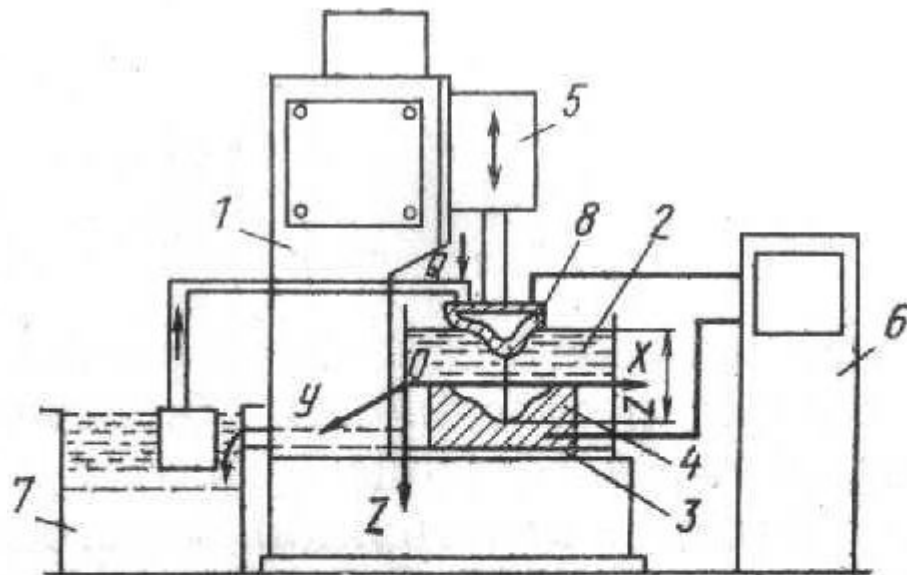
Схема изготовления объемно-профилированной матрицы на электроэрозионном копировально-прошивочном станке ( $x, y, z$  — координаты перемещения электрода-инструмента): 1 — станок; 2 — ванна с диэлектрической жидкостью; 3 — стол для установки заготовки (электрод-деталь); 5 — регулятор подачи; 6 — генератор импульсов; 7 — система снабжения диэлектрической жидкостью (насосы, фильтры, бак); 8 — электрод-
